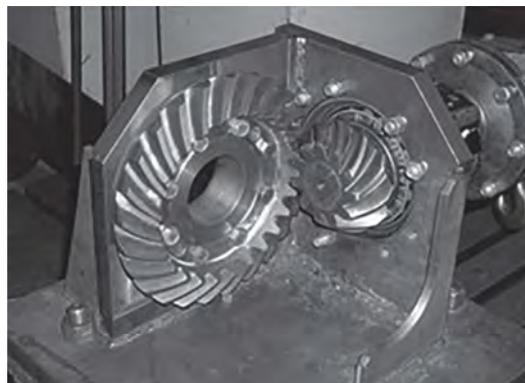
Вал-шестерня главной передачи автомобиля MAZ-5551 (деталь 5551-2402017)
